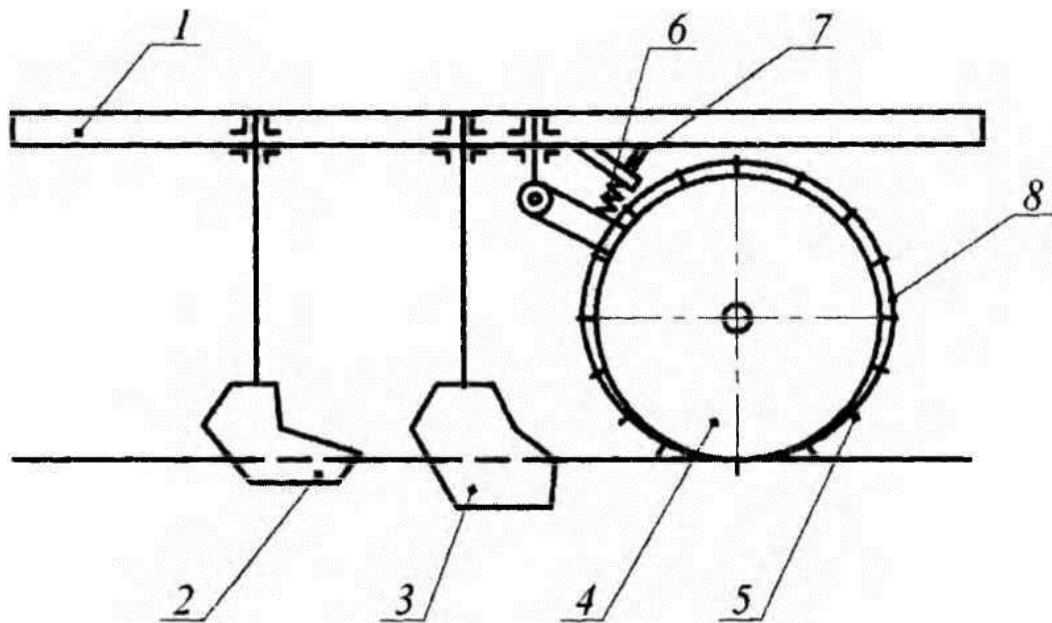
Пристрій для обробітку міжрядь [5], вид збоку
